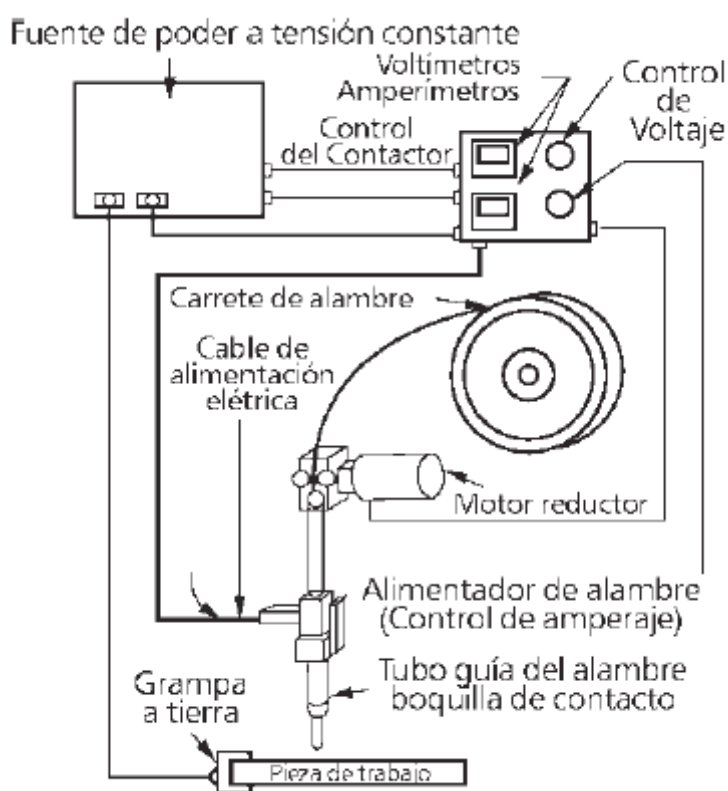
Equipo para hacer soldadura al arco con núcleo de fundente
